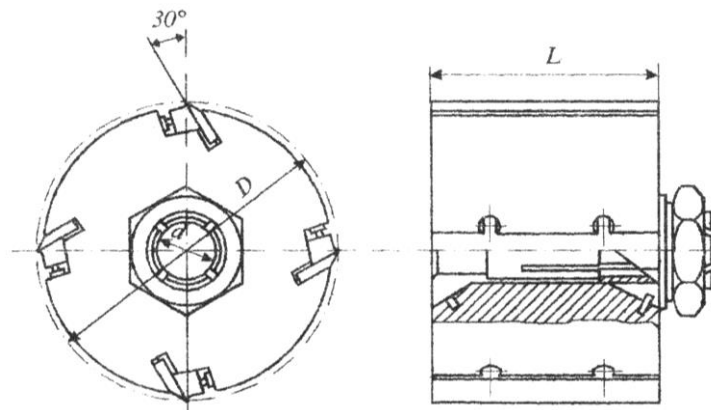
Конструкція збірної насадної фрези для плоского фрезування:
